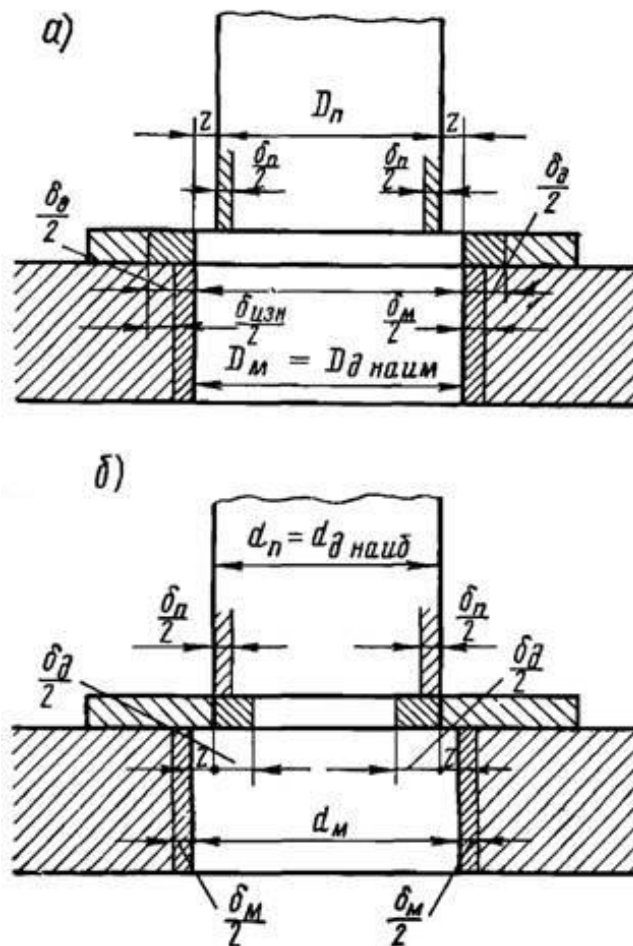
Схема расположения зазоров и полей допусков на изготовление рабочих частей штампов: а— при вырубке наружного контура; б — при пробивке отверстия; δ_{Π} — допуск на изготовление пуансона; δ_{δ} — допуск на изготовление матрицы; δ — допуск на изготовление детали
